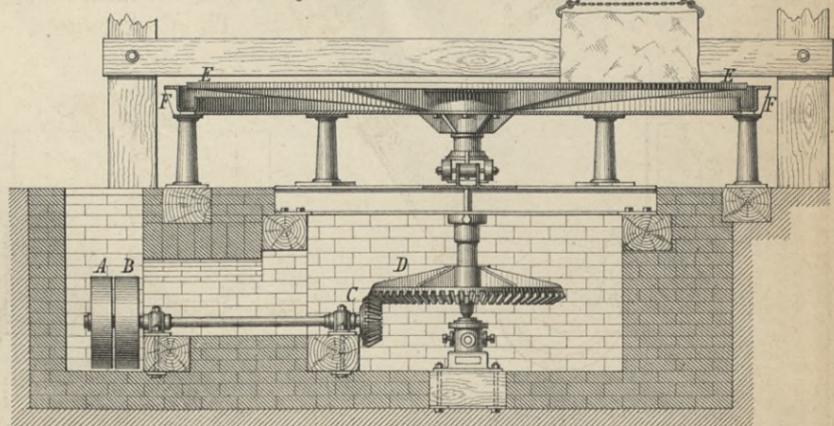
u. 17. Lloyd's Schmirgelfräsmaschine für Backsteine. Fig. 17.
